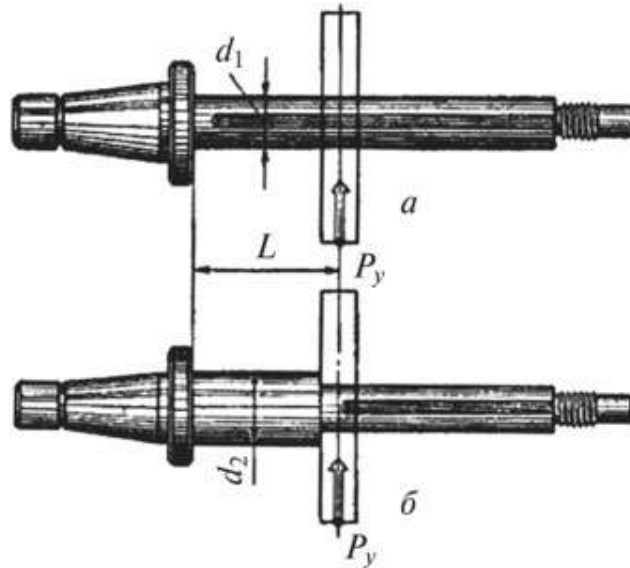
Схема фрезерних оправок: а - Звичайна; б - підвищеної жорсткості
